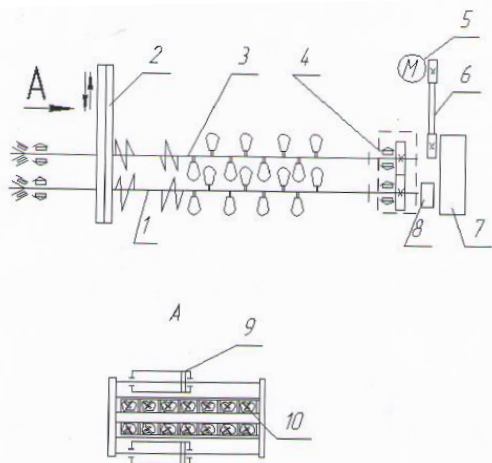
Глиномешалка с фильтрующей решеткой: 1-вал, 2-головка фильтрующая, 3-вал, 4-коробка раздаточная, 5-двигатель, 6-передача клиноременная, 7-редуктор, 8-муфта, 9-гидроцилиндр, 10-решетка
